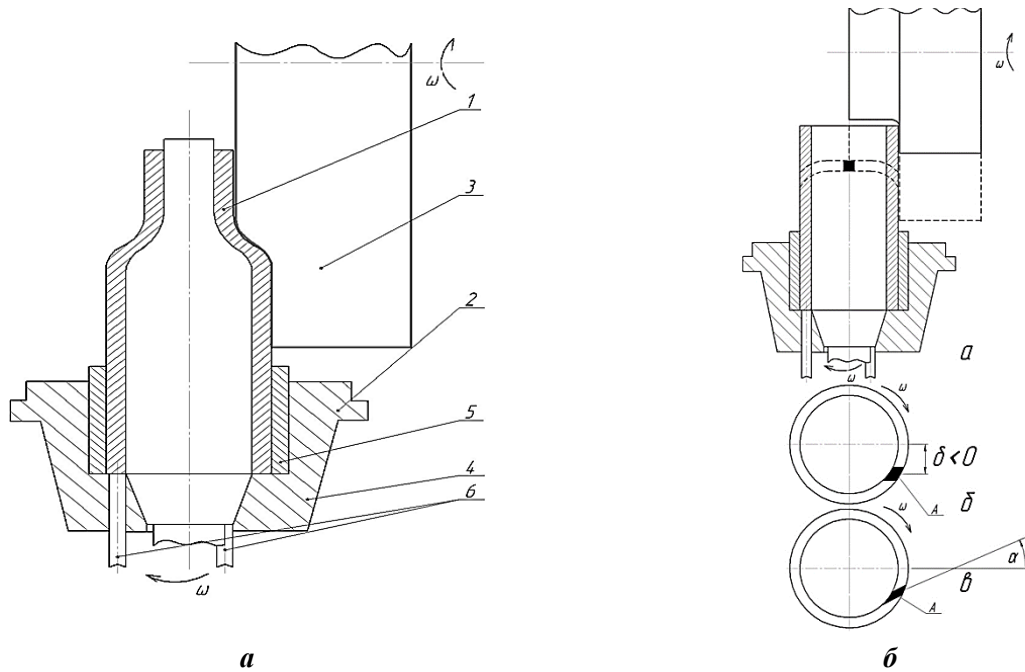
Технологічні схеми обкочування труб циліндричним роликом: а) формування днища трубної заготовки; б) формування горловини трубної заготовки
